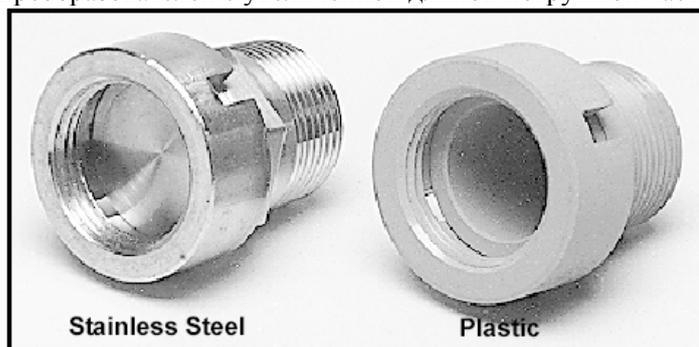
Стандартные заглушки Pan-Adapta с нарезанной резьбой из нержавеющей стали (слева) и из пластика (справа)
